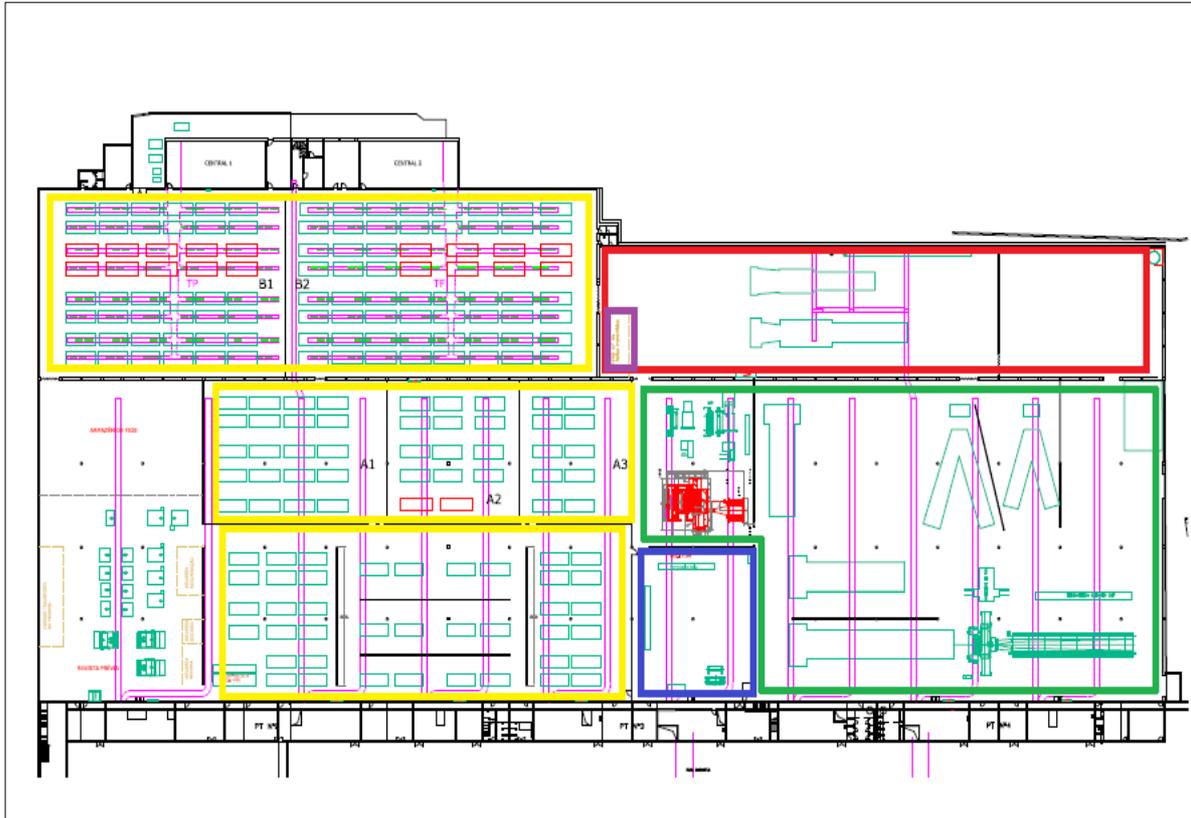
Layout da secção da tecelagem da empresa (anexo V)
